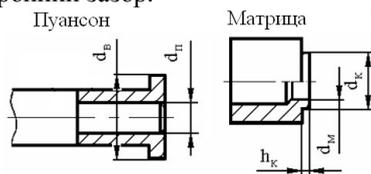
Инструмент для получения соединений недеформируемыми заклепками
